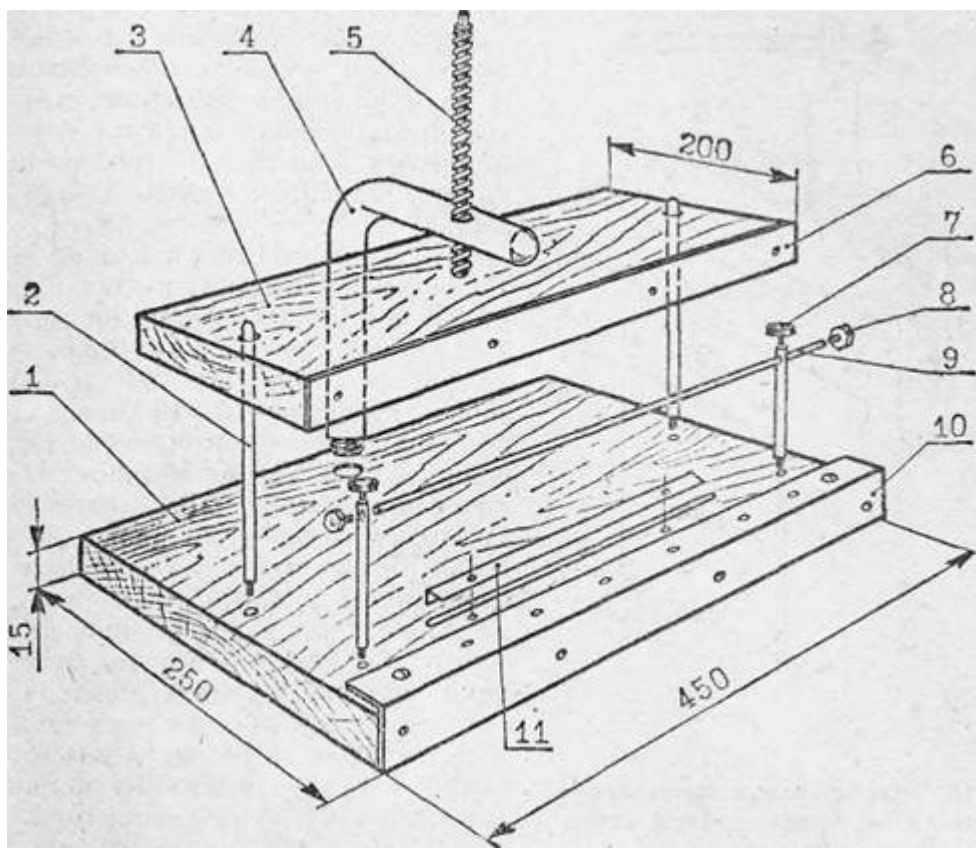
Универсальный переплетный станок: 1 – нижняя плита; 2 – направляющая стойка; 3 – верхняя (подвижная) плита; 4 – кронштейн; 5 – упорный винт; 6 – линейка для обрезки блока; 7 – зажимный винт; 8 – рукоятка; 9 – вал; 10 – уголок; 11 – фиксатор
